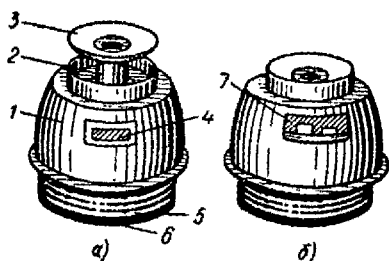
Клапан термостата с жидким наполнителем (общий вид): а – основной клапан открыт; б – основной клапан закрыт; 1 – корпус коробки термостата; 2 – стержень; 3 – основной клапан; 4 – вспомогательный клапан; 5 – сильфон; 6 – нижняя крышка коробки; 7 – окно для прохода жидкости при открытии вспомогательного клапана
